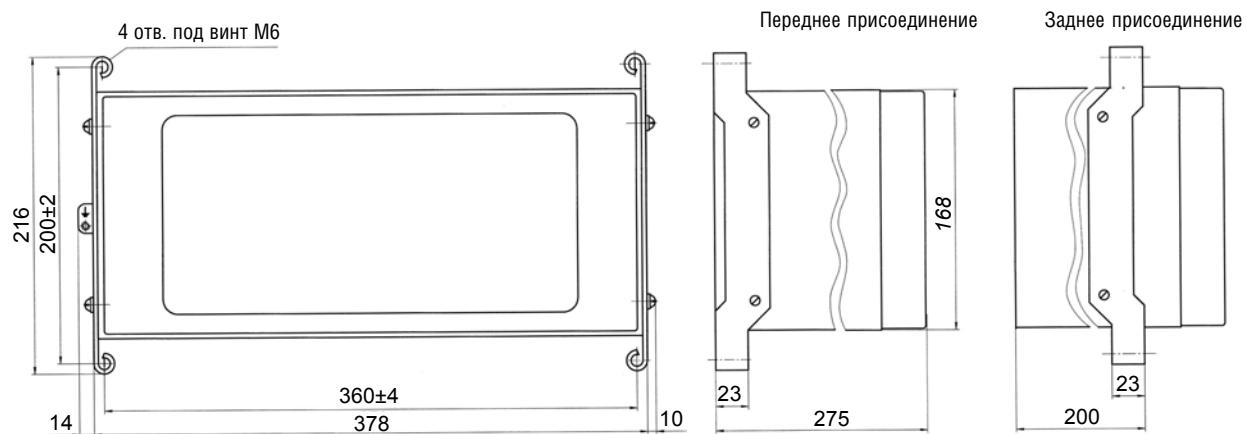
Габаритные, установочные размеры блоков типов БЭ 1101, БЭ 1102, БЭ 1103.
